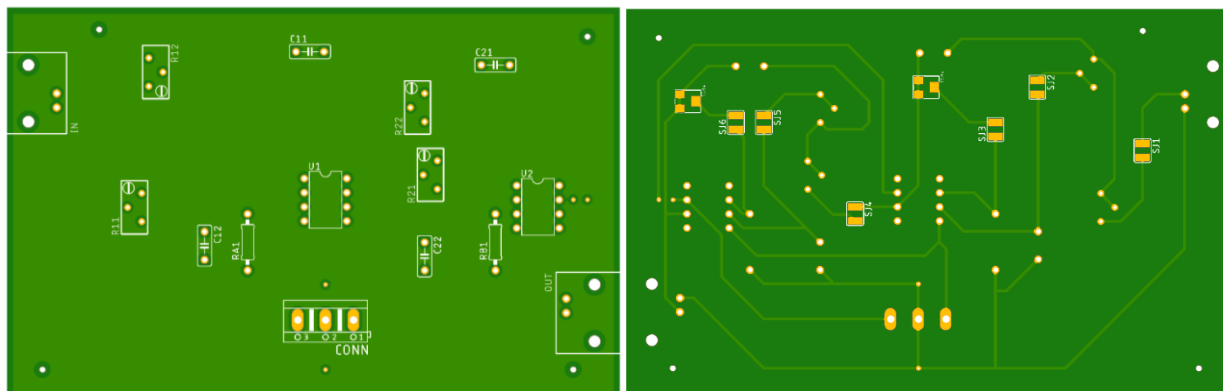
Render de la PCB en dues dimensions (Esquerra: capa top, Dreta: capa bottom)
